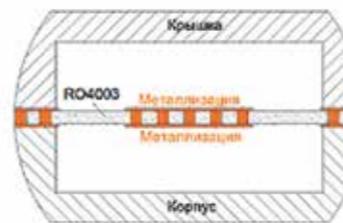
Разрез конструкции линии передачи мощного СВЧ сигнала
